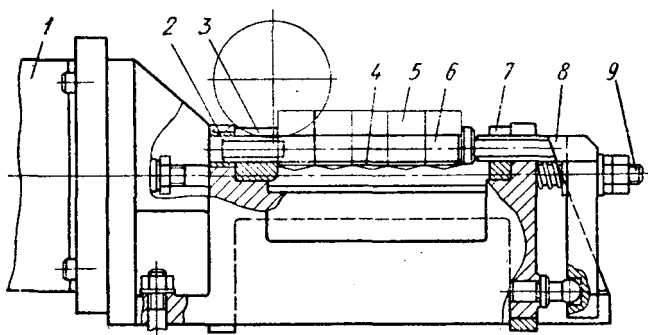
Универсально-наладочное фрезерное приспособление со сменными оправками
